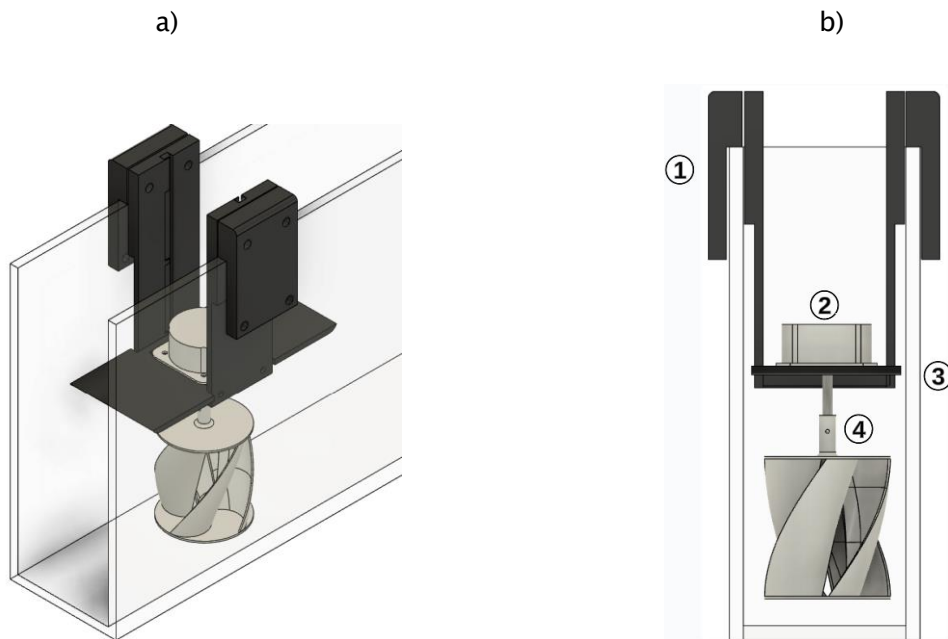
Estructura para montaje de turbinas. a) Vista Isométrica, b) Vista Frontal seccionada.
